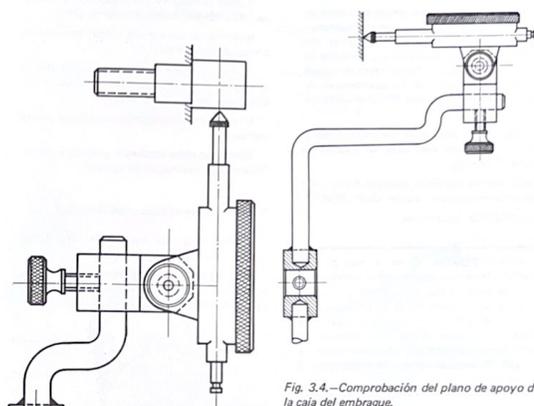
Comprobación del plano de apoyo de la caja del embrague.
